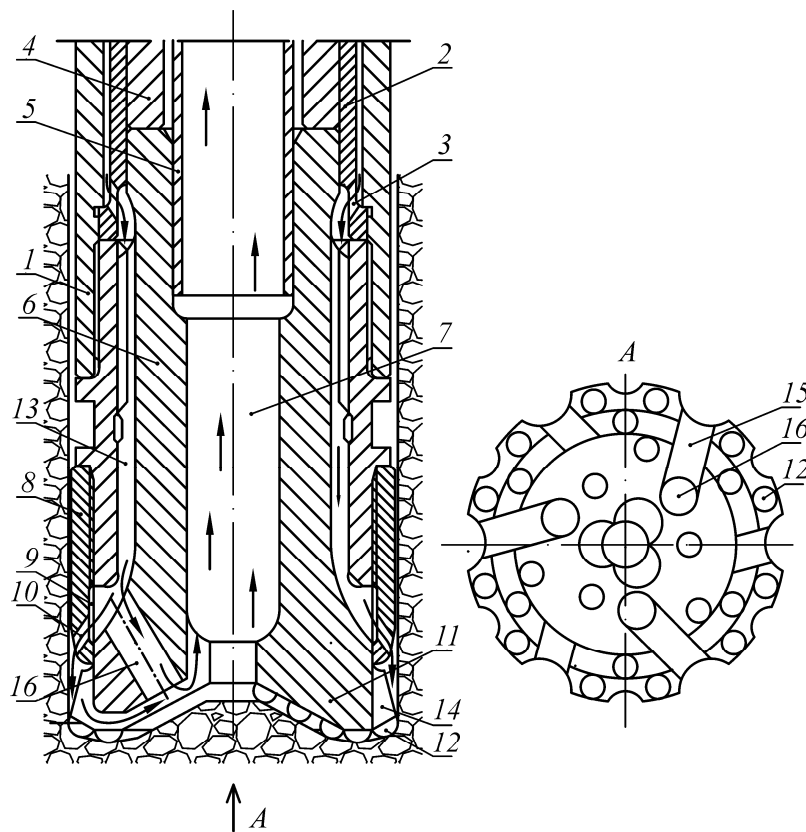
Забойная часть пневмоударника с обратной циркуляцией очистного агента: 1 — корпус; 2 — гильза; 3 — выхлопные отверстия; 4 — ударник; 5 — центральная шламотранспортная труба; 6 — буровое долото; 7 — центральный шламоприемный канал; 8 — призабойный пакер; 9 — кольцевая камера; 10 — продувочные каналы; 11 — головная часть бурового долота; 12 — породоразрушающие вставки; 13–15 — продувочные пазы; 16 — продувочные каналы
